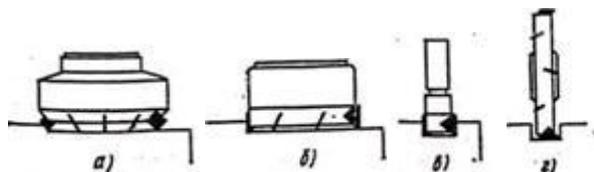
Набор фрез с неплетачиваемыми пластинками
